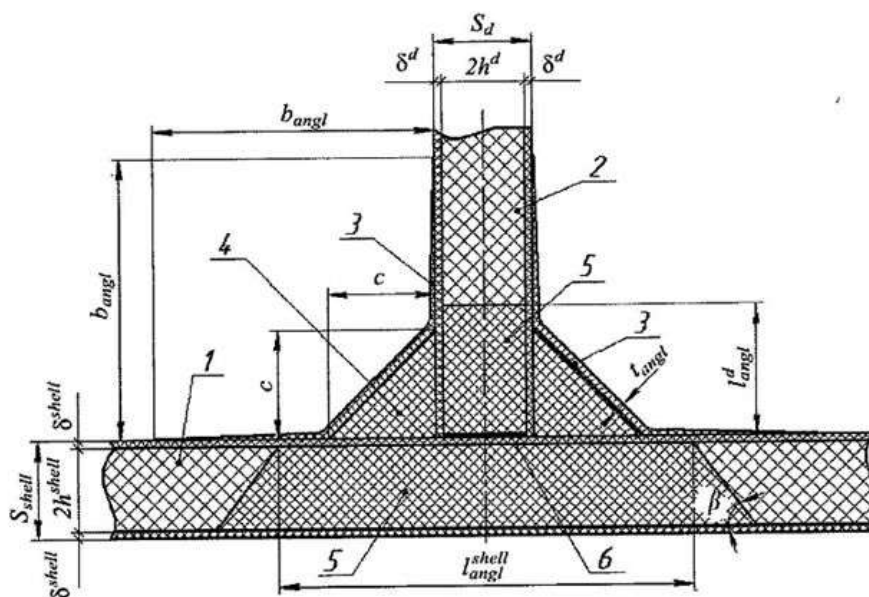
Вузол з'єднання обшивки корпусу і перегородки тришарової конструкції: 1 - обшивка; 2 - перегородка; 3 - приформовочні косинці; 4 - опорні елементи; 5 - закладні елементи; 6 - адгезійна речовина
